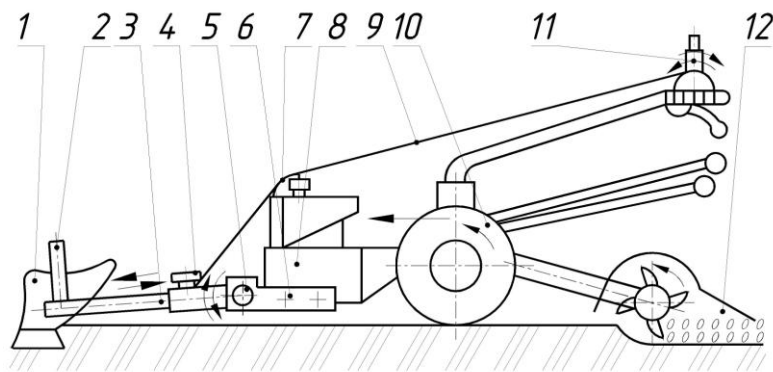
Стабілізуючий пристрій з плужними корпусами до мотоблока:
